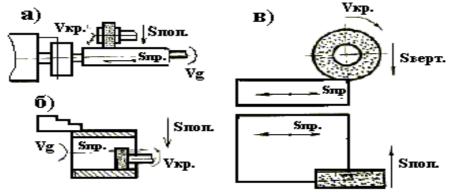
Схемы шлифования: а) наружное круглое; б) внутреннее круглое; в) плоское.
